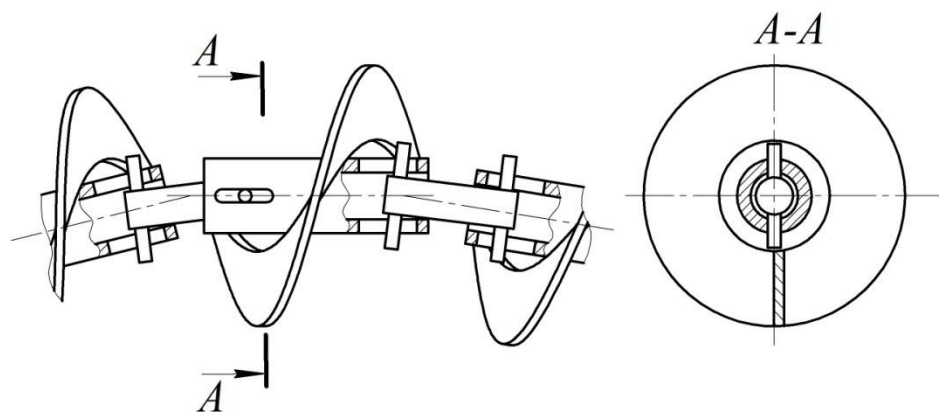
Шарнірний робочий орган з радіальними пальцевими елементами зачеплення
